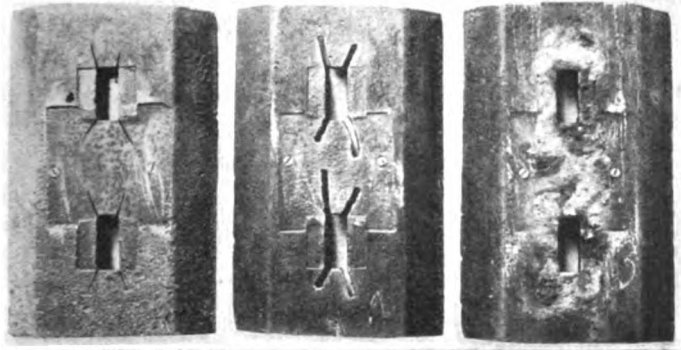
Schwelleninstandsetzung durch autogene Schweißung.
